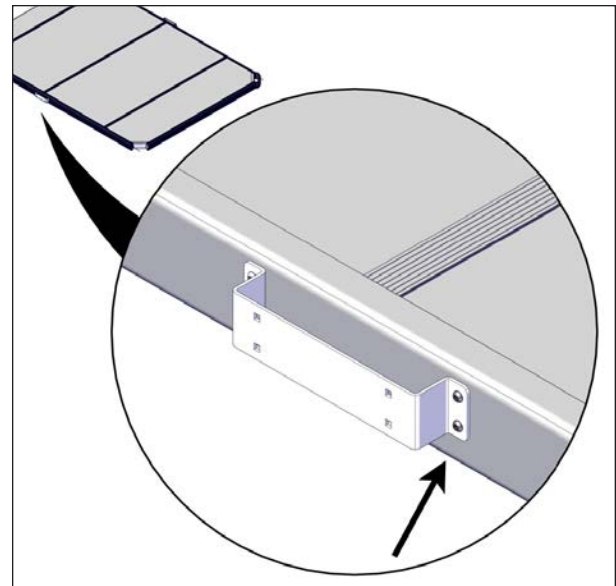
SERRAGE DES VIS DU SUPPORT DE MONTAGE
